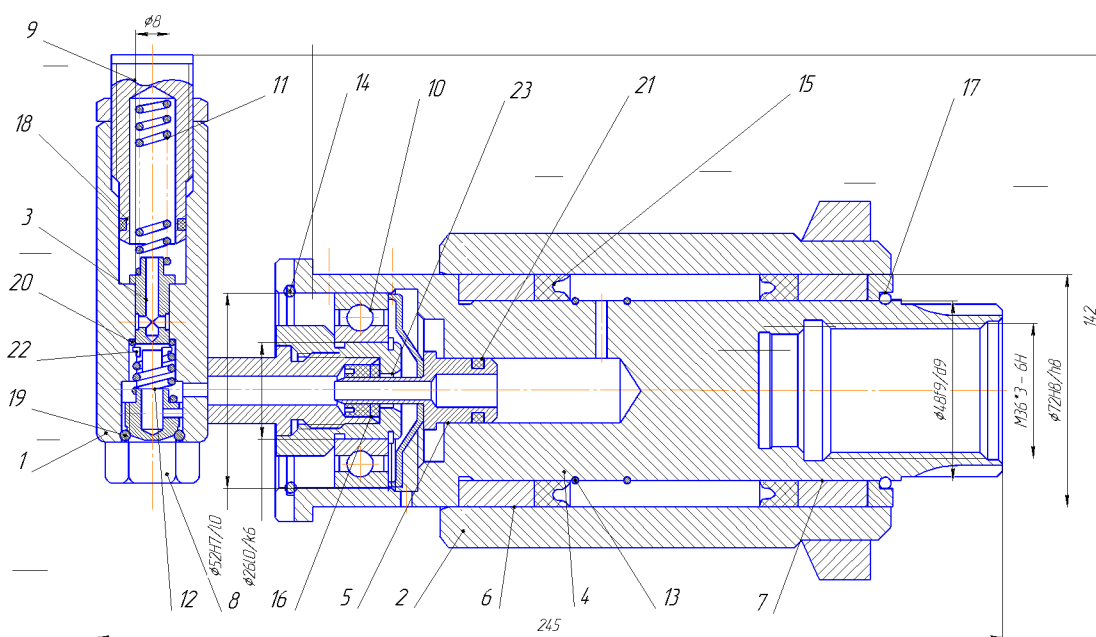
Загальний вид гідроциліндра варіатора
